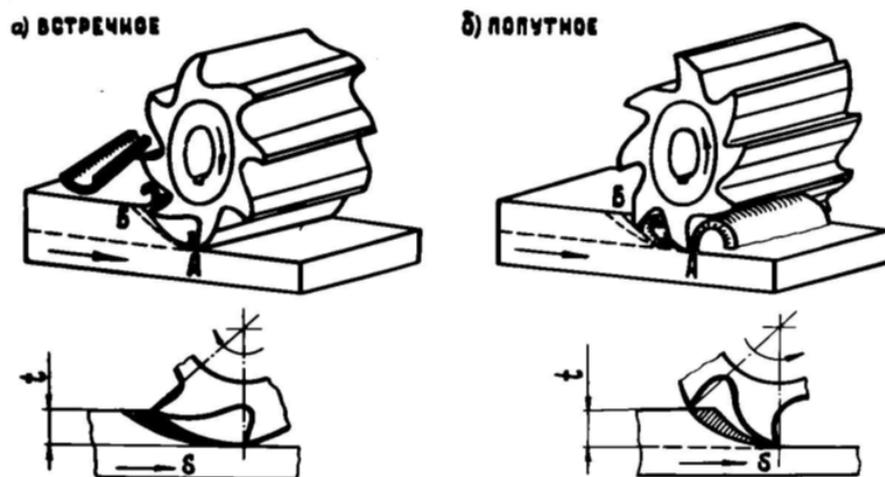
Схемы фрезерования: а – встречного; б – попутного
